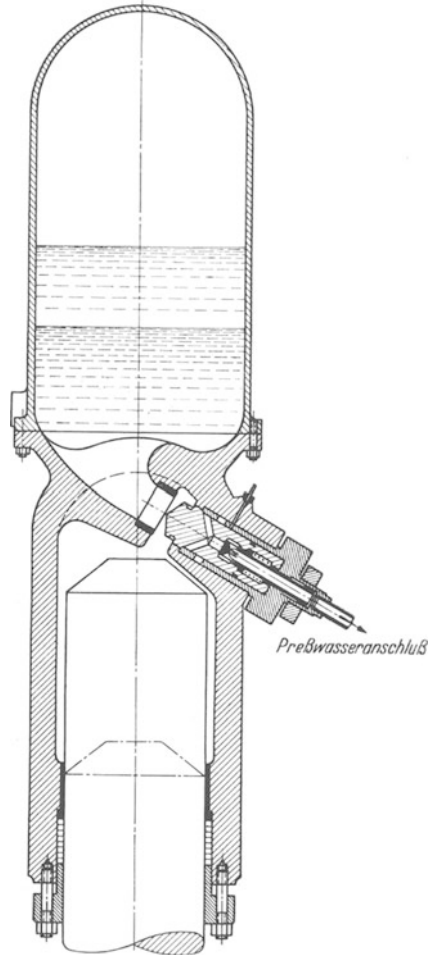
Preßzylinder mit aufgebautem Windkessel und Füllventil im Zylinderholm. (Banning A. G., Hamm i. W.)
